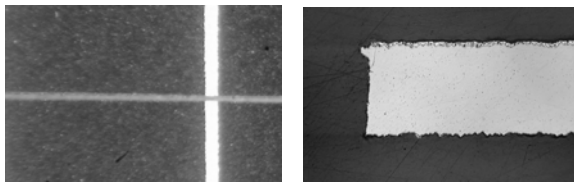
Laser-Microjet®: Schnittfuge, Breite der Fuge ca. 0,1 mm (links) Schliffbild quer zu einer Schnittfläche (rechts)
